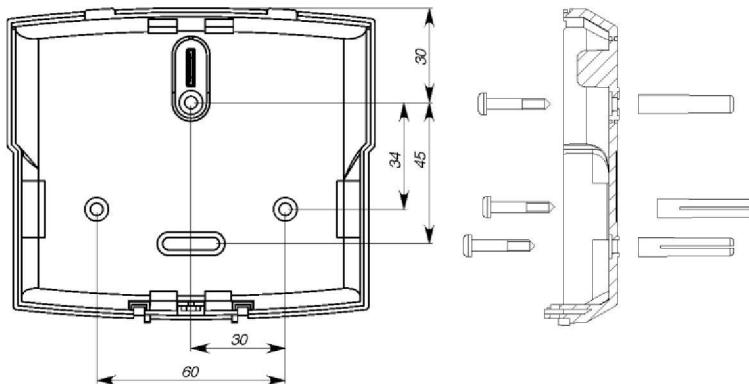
Разметка крепежных отверстий для клавиатуры М4064КР
